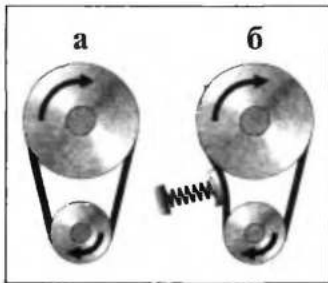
Цепной привод распределительного вала двигателей OHV: а — без натяжителя; б — с натяжителем цепи
